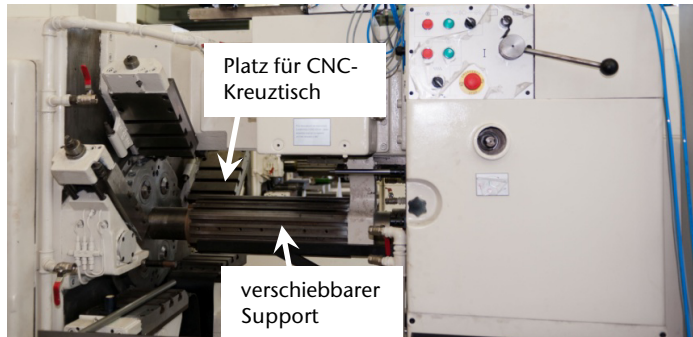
Freiraum der Werkzeugmaschine für den Ausbau vor dem Retrofit
